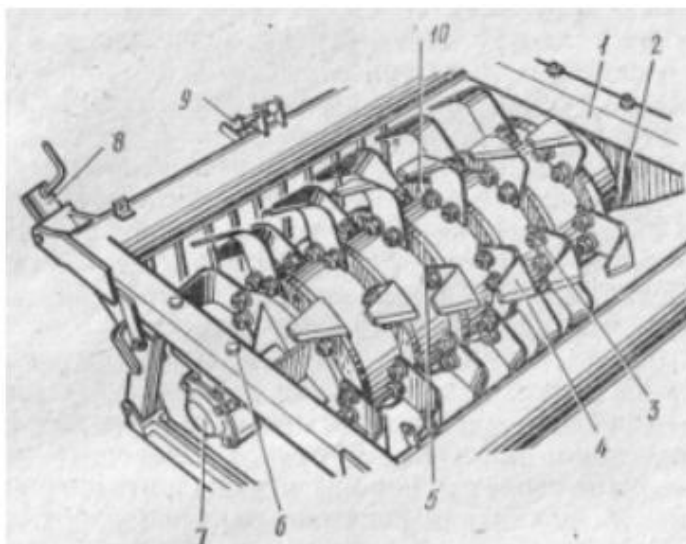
Барaban фрезы ФБН-1,5: 1 — брус рамы; 2 — хомут; 3 — болт крепления ножа; 4 — нож; 5 — диск; 6 — болт крепления корпуса подшипника барабана; 7 — корпус правого подшипника; 8 — регулировочный винт глубины фрезерования; 9 — винт регулировки наклона решетки; 10 — отверстие для установки ножей.
